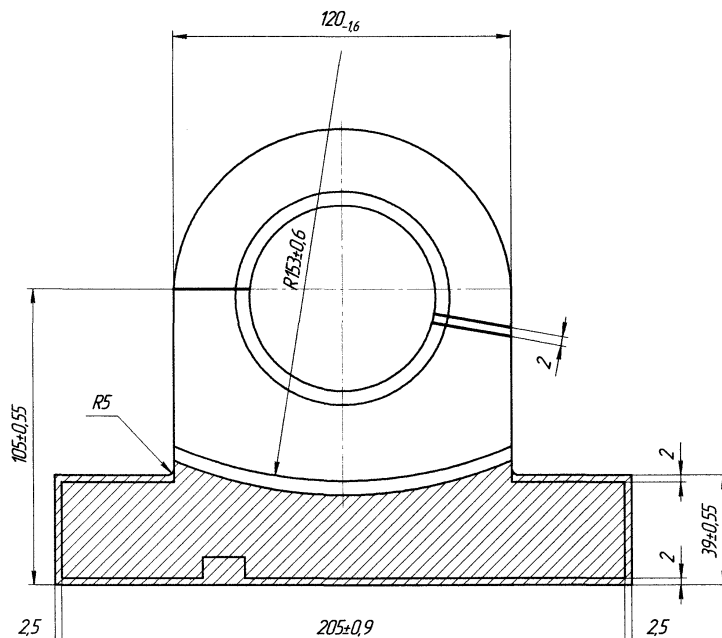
Ескіз проектної заготовки - переріз А-А
